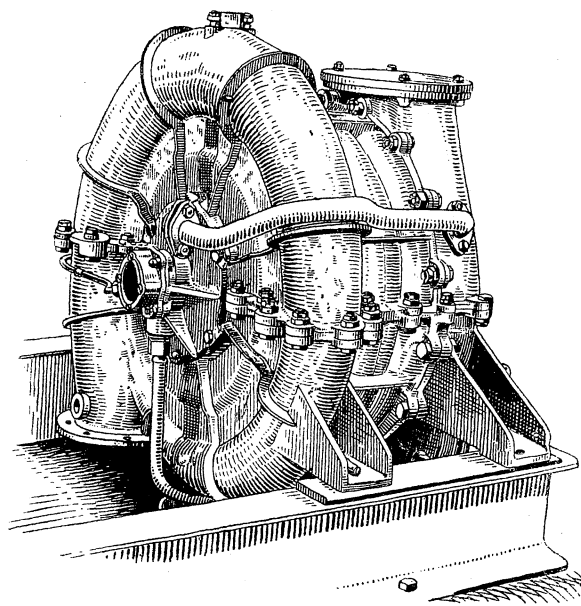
Gebläse für einen 350 PS-Flugmotor mit abwärts gerichteten Druckstutzen.
